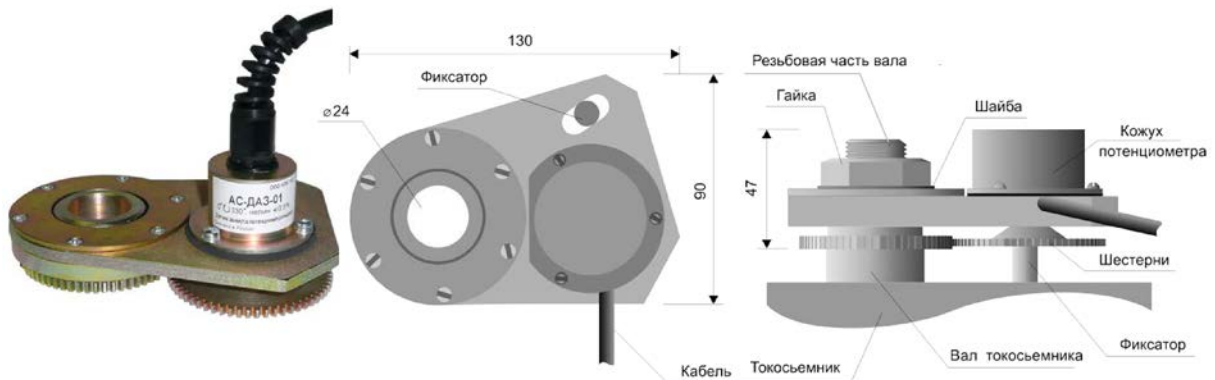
Внешний вид и габариты датчика азимута платформы АС-ДАЗ-01
